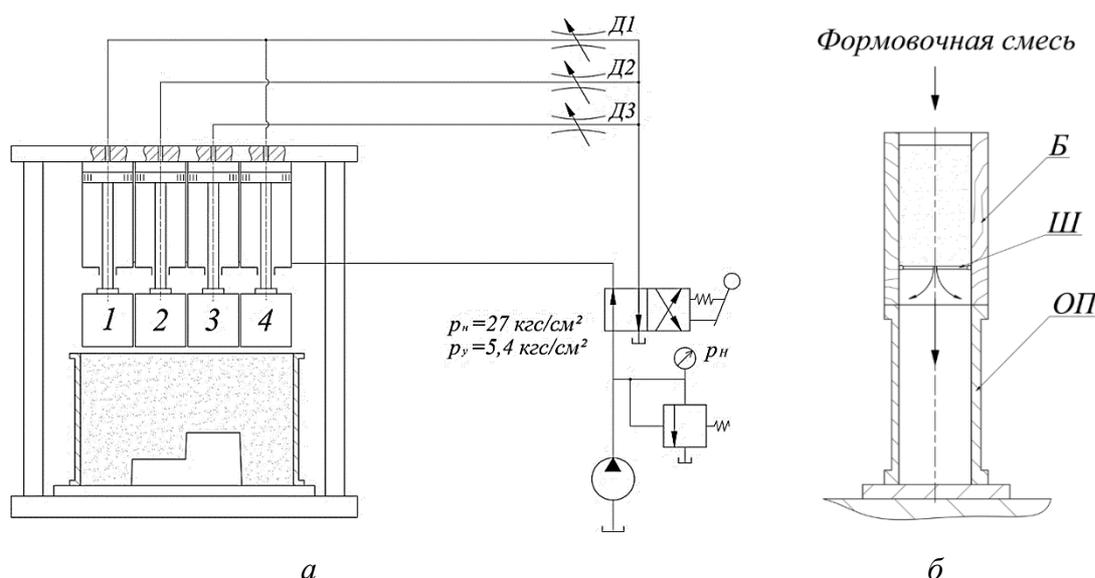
Лабораторная установка: а – конструкция установки и гидравлическая схема привода; б – схема гравитационной подачи формовочной смеси из бункера Б в опоку ОП с использованием шторного затвора Ш
